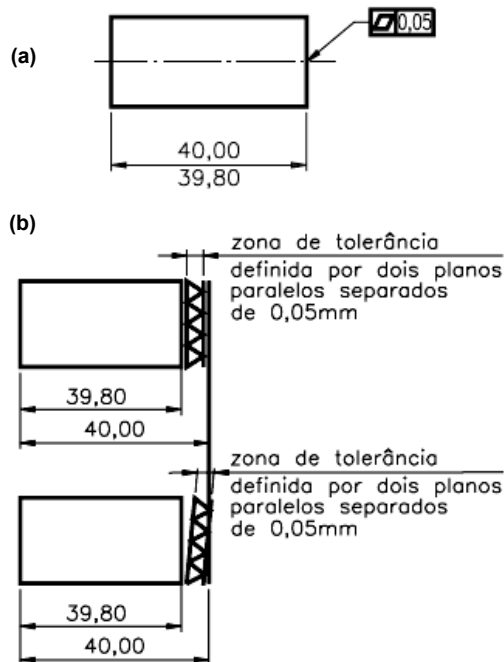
Desenho representativo da condição de planeza, com tolerância de planeza (a) e tolerância dimensional (b).
